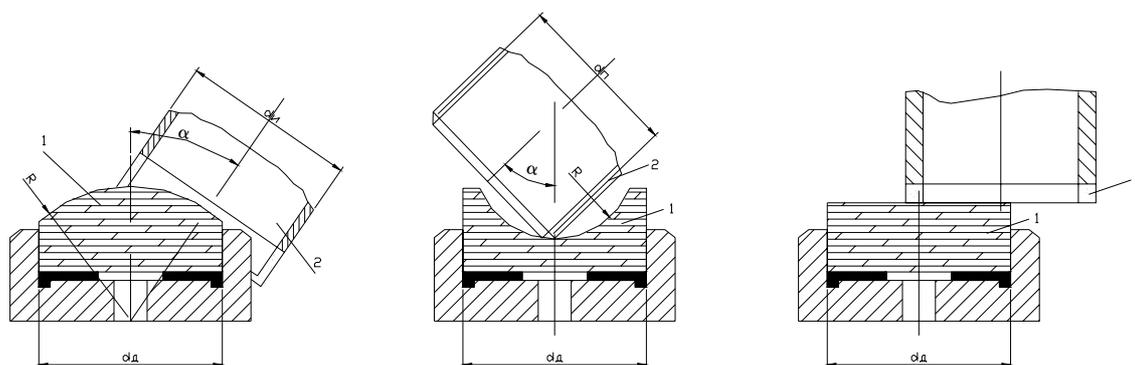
Схема обработки с жестко устанавливаемым инструментом
